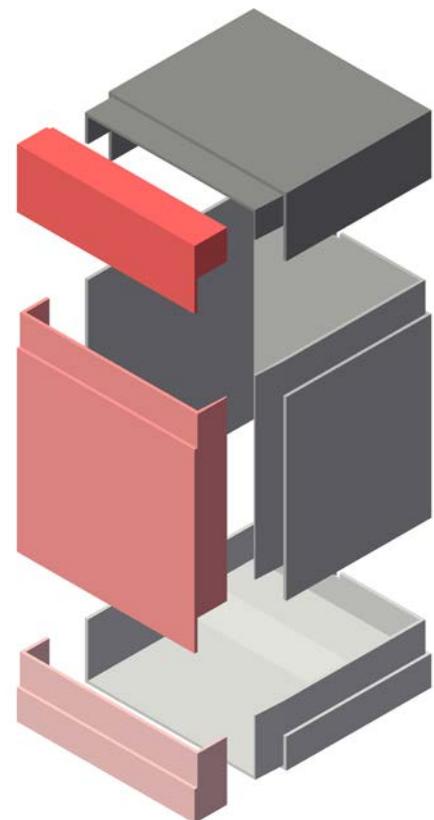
Prinzipskizze eines mit VSI gedämmten Kühlschranks
